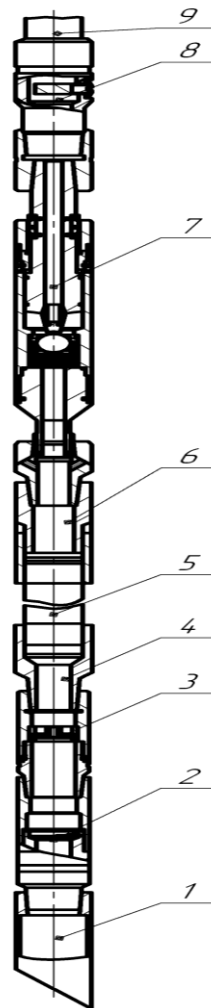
Комплекс пристроїв для очищення вибою свердловин
